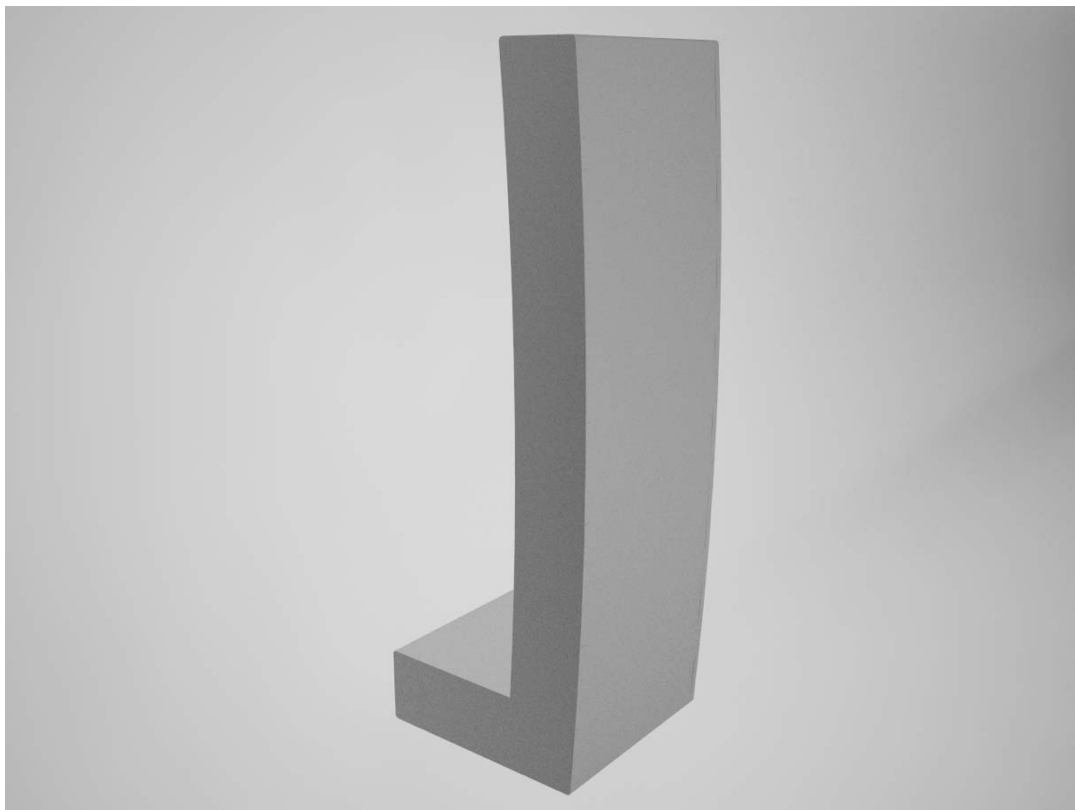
Vista in sezione generale del modulo applique a parete
